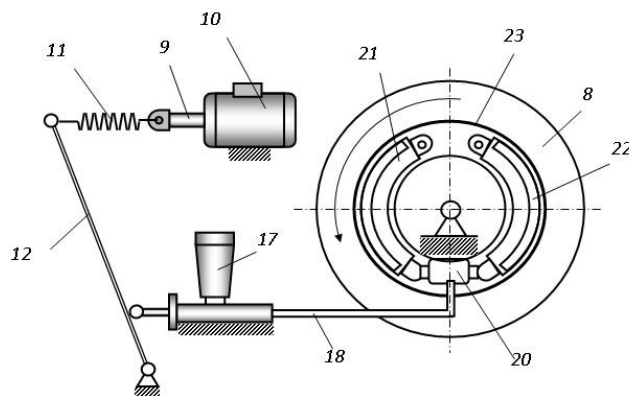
Схема тормозного механизма стенда для проведения имитационных испытаний гидроцилиндров:
